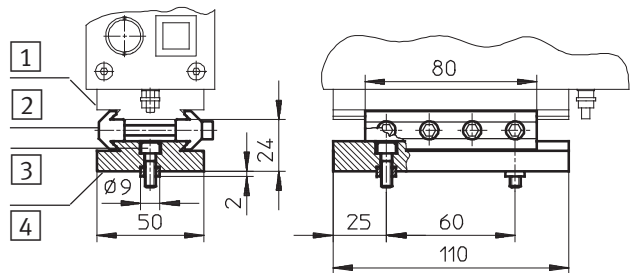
/2: Befestigung der Checkbox mit Verbindungsbausatz HMSV-12
